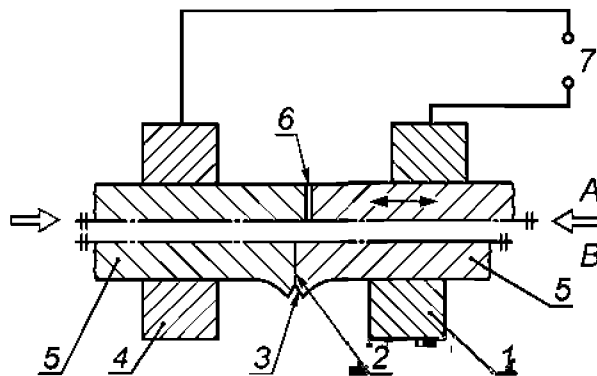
Сварка контактная рельефная двусторонняя
